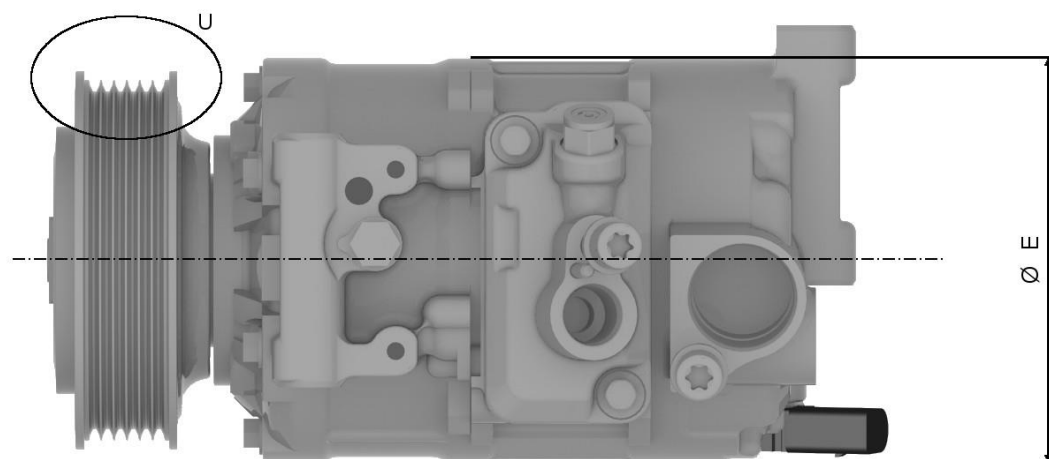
Установочные размеры компрессора климатической установки (вид сверху)
